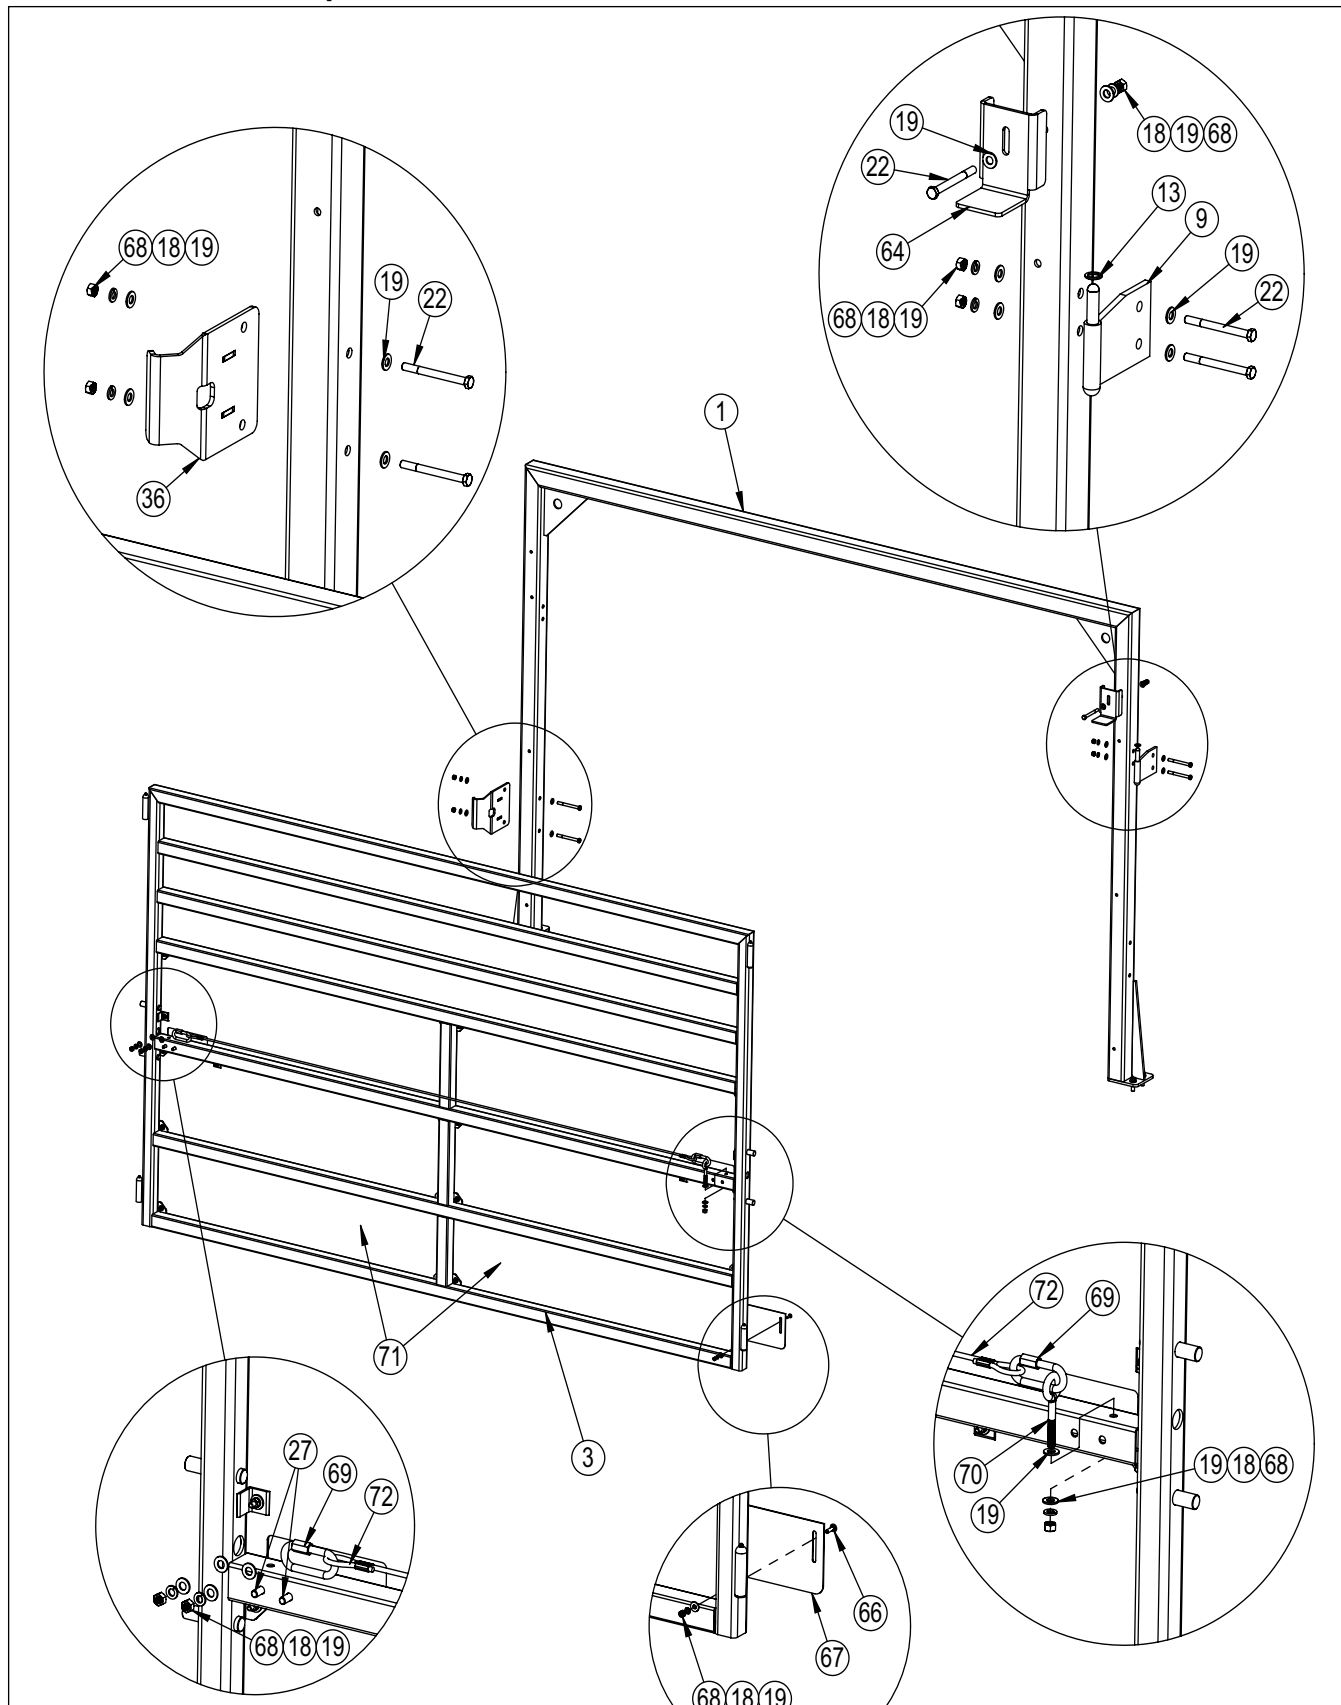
Illustration des pièces des barrières de la balance MAS-LC
